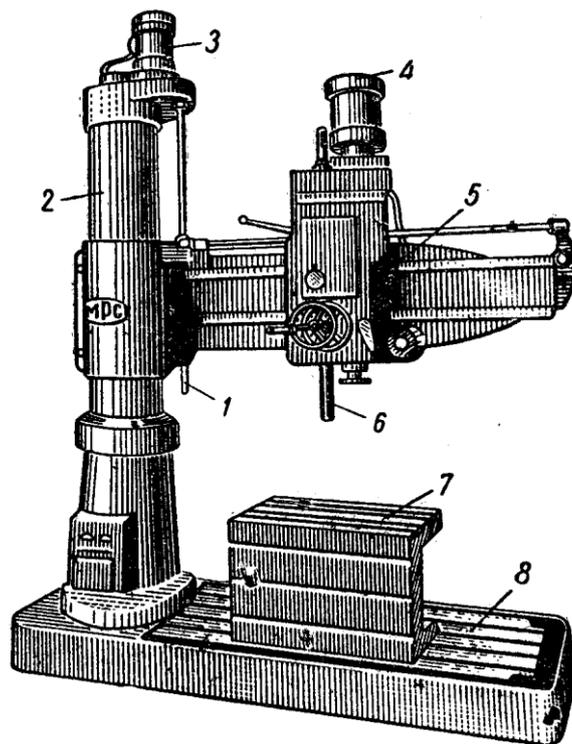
Общий вид радиально-сверлильного станка: 1 – винт; 2 – колонна; 3, 4 – электродвигатель; 5 – рукав; 6 – шпиндель; 7 – стол; 8 – фундаментная плита
